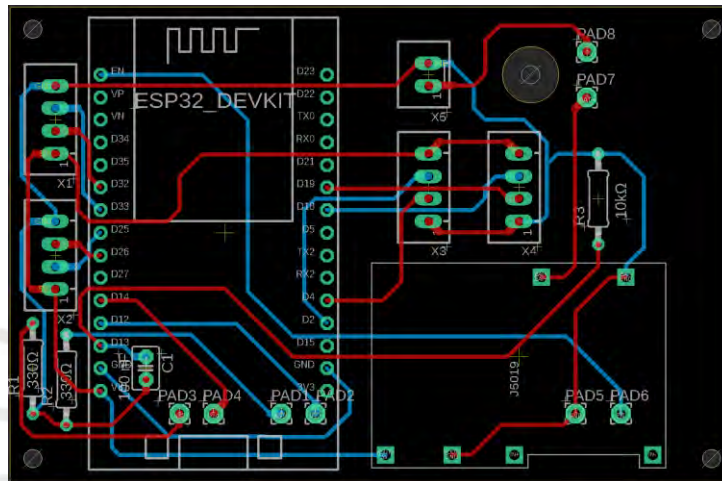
Tarjeta PCB del accesorio medidor del alcance de remado. Fuente: Elaboración propia.
